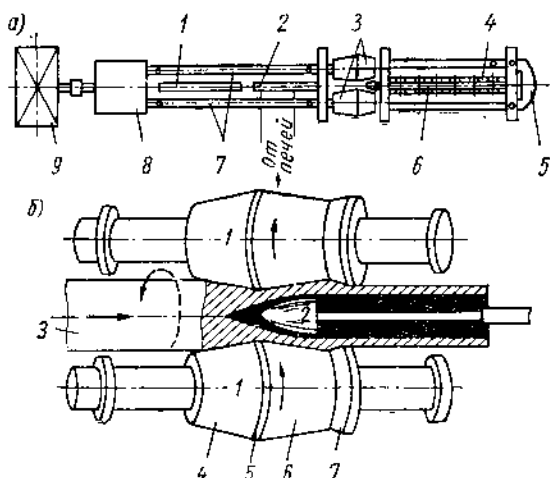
Схема прошивки заготовок и расположения прошивного стана с бочкообразными валками: а — схема расположения стана:
